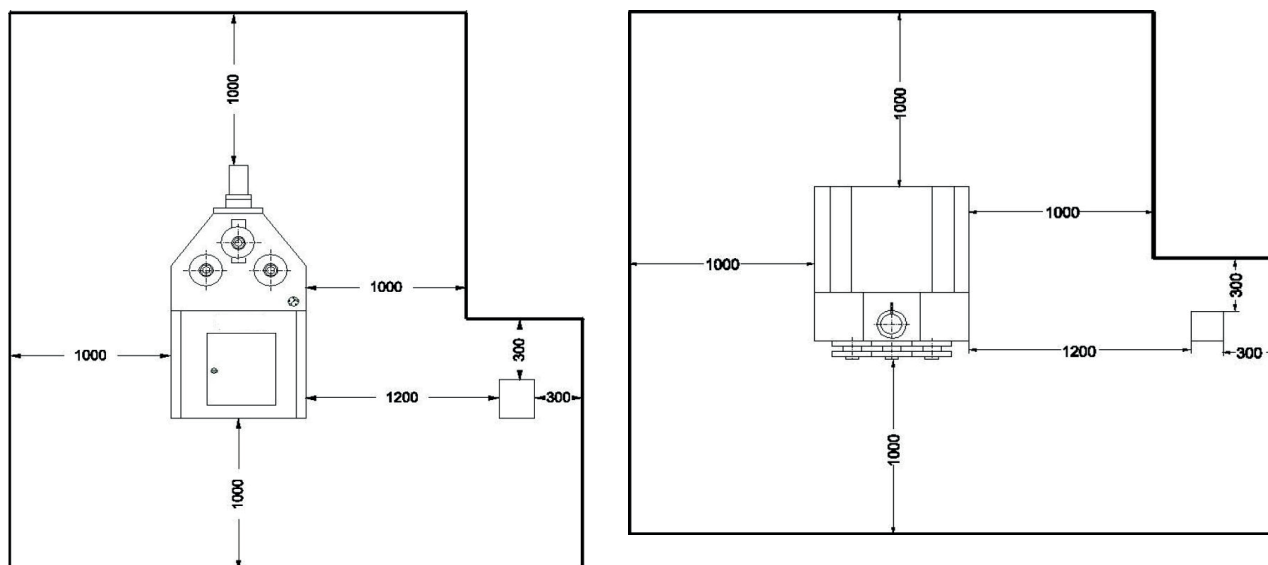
Dimensions de l'espace de travail - Installation verticale (à gauche) et horizontale (à droite)
